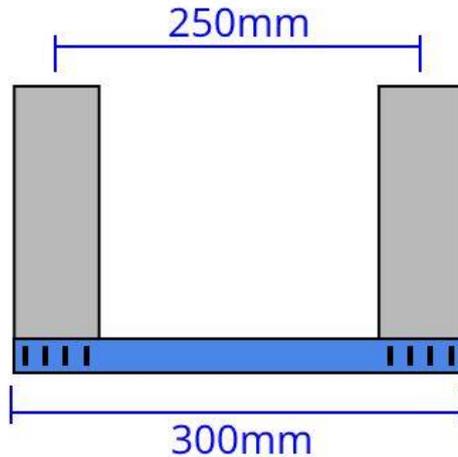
Esquema de medidas en la unión entre PCB conexión vertical y PCB conexión horizontal.
